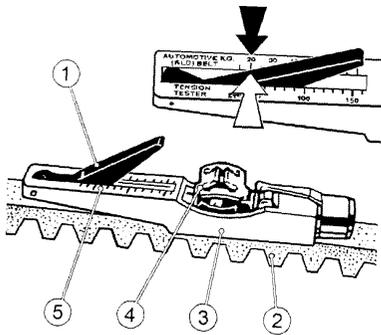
Приспособление Optikrik для проверки натяжения приводных ремней:
